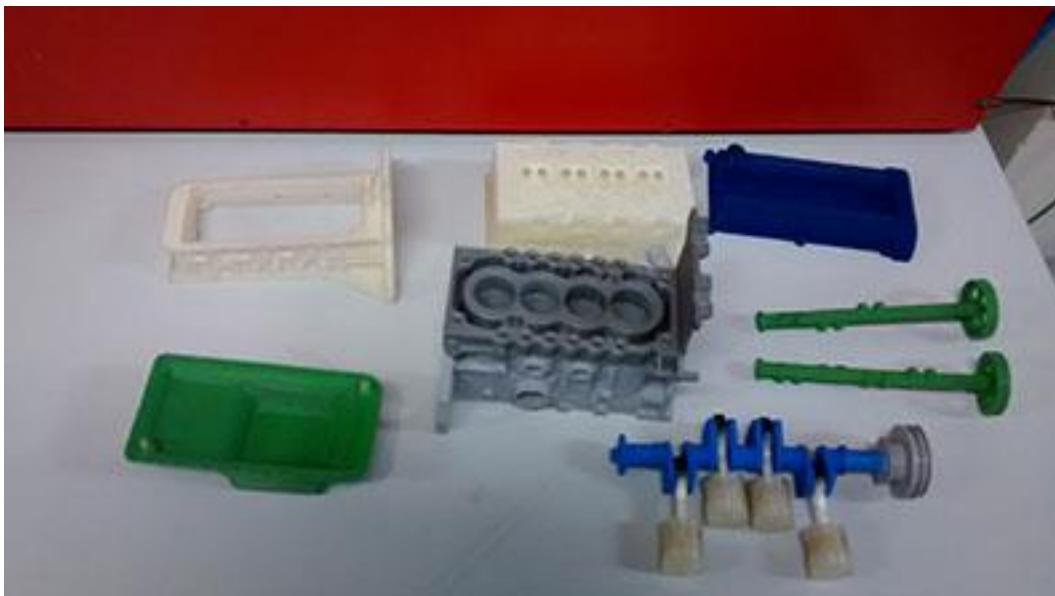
Peças Principais do Motor Aguardando Montagem.
